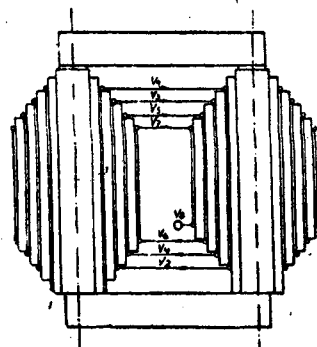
Расположение обмоток высоковольтного трансформатора конструкции проф. Фишера.
